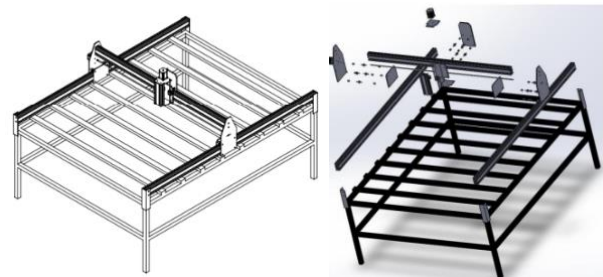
Gráfico de ensamble en SolidWorks del centro de mecanizado CNC.
